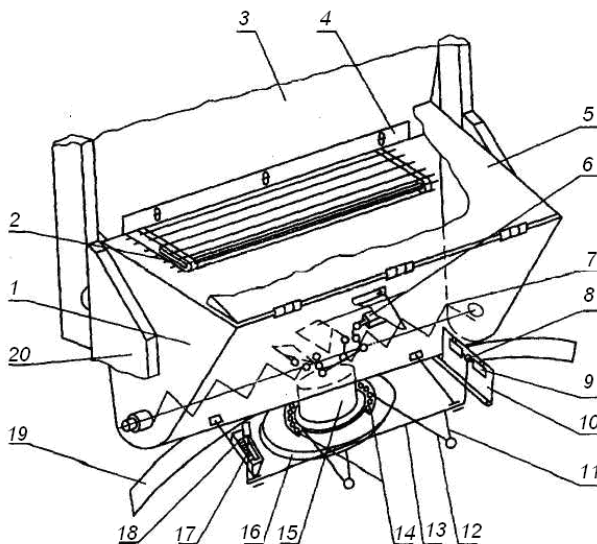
Навесной разбрасыватель удобрений: 1 – бункер; 2 – транспортер; 3 – задний борт транспортного полуприцепа; 4 – регулировочная планка; 5 – крышка; 6 – датчик заполнения бункера; 7 – шнек; 8 – рычаг гидроуправления; 9 – гидроцилиндр управления дозирующими заслонками; 10 – панель гидроцилиндров; 11 – поводок; 12 – талреп; 13 – поворотный вал; 14 – маркированные отверстия; 15 – выходной патрубок; 16 – рассеивающий конусный диск; 17 – рычаг ручного управления; 18 – шкала; 19 – отражатель удобрений; 20 – рама навесного разбрасывателя
